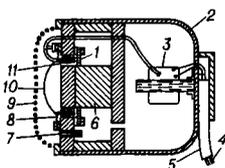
Катушечный электродинамический микрофон (разрез): 1 – акустическое сопротивление; 2 – корпус; 3 – трансформатор; 4 – выводы; 5 – кабель; 6 – магнит; 7 – акустический канал; 8 – гофрированный воротник; 9 – защитный кожух; 10 – диафрагма; 11 – звуковая катушка
